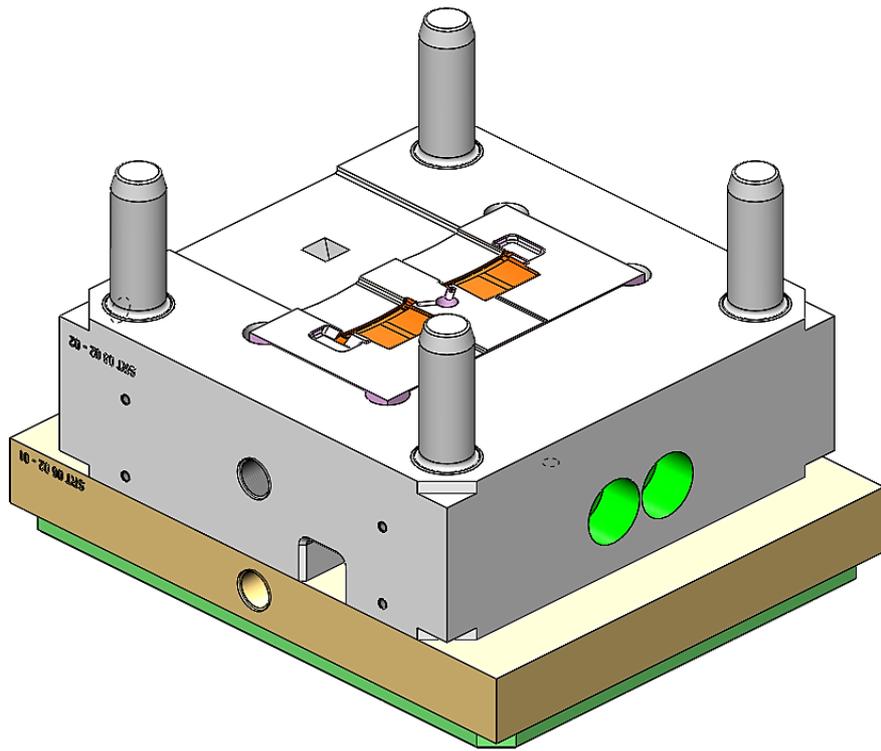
Cavidade do molde que sobreinjeta a peça com SEBS.
